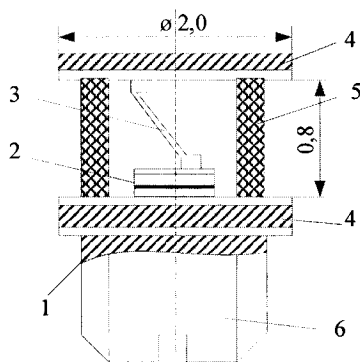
Конструкція одного із типових ЛПД для частот до 18 ГГц (усі з'єднані поверхні металізовані під паяння)
